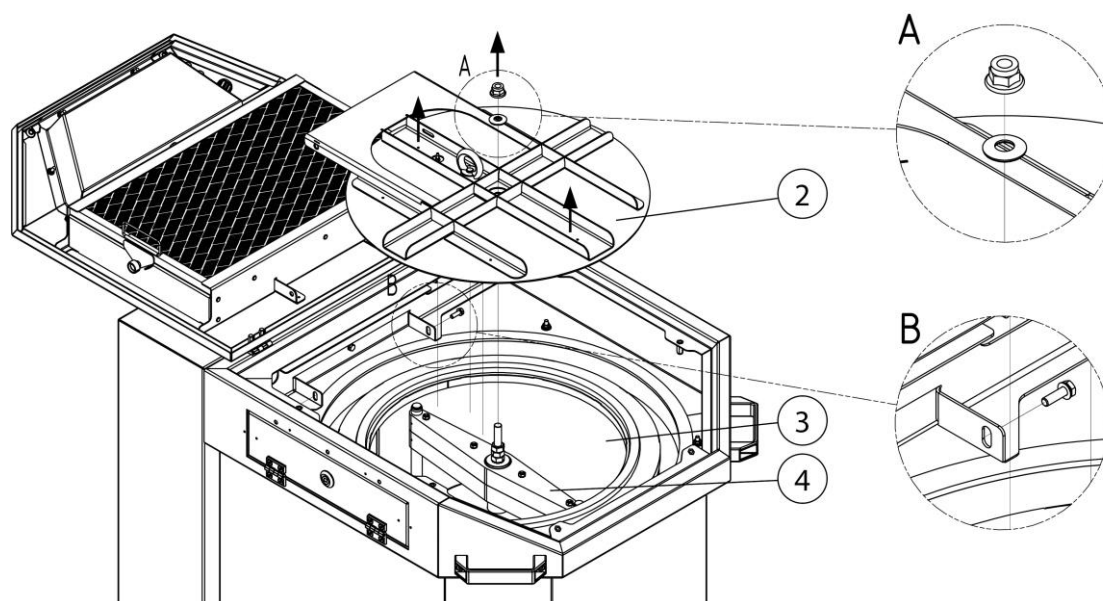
Cambio de filtro - Desmontaje de la tapa de filtro
